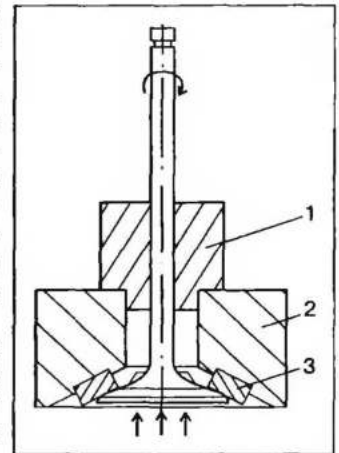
Общая схема обработки фаски клапана резцовой головкой: 1 — центрирующая втулка; 2 — резцовая головка; 3 — твердосплавный резец
